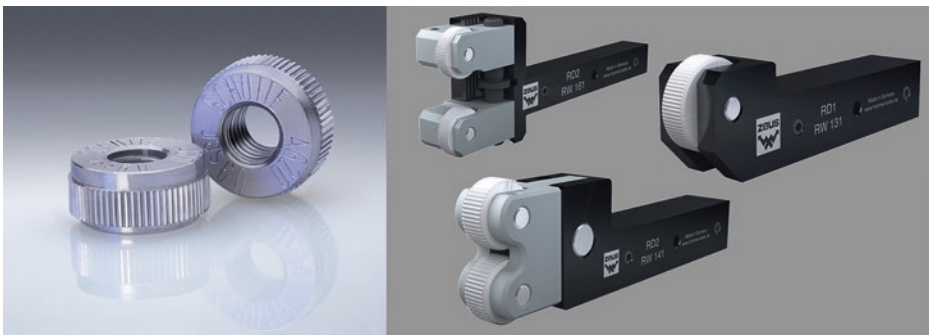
Werkstück mit radialer Rändelung und axialer Stempelung (links) [Schu08] und Rändelwerkzeuge (rechts) [Homm18]
